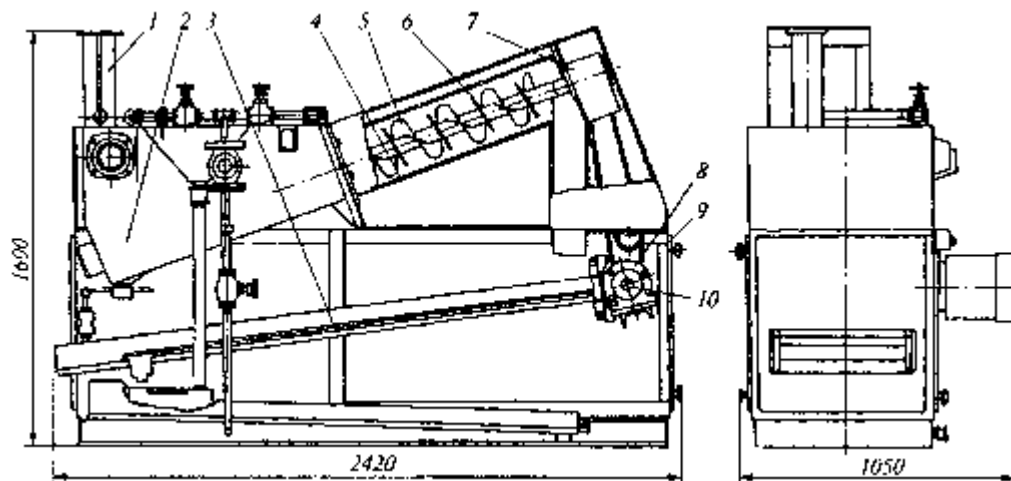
Моечная машина А1-БМГ. 1 - питатель, 2 – моечная ванна, 3 – ситовой кузов и система трубопроводов, 4 – сварной корпус, 5 – моющий шнек, 6 – лопатки для перемешивания крупы, 7 – редуктор, 8 – электродвигатель, 9 – станина
